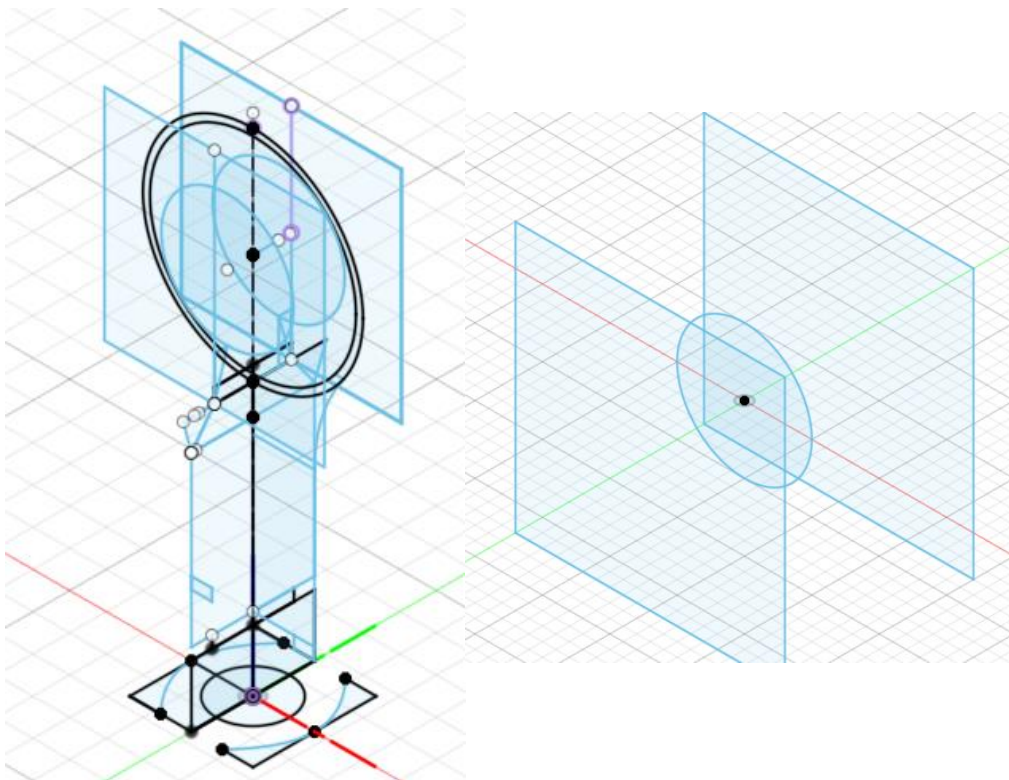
Το Drawing για το Circlip του Clevis Joint.
